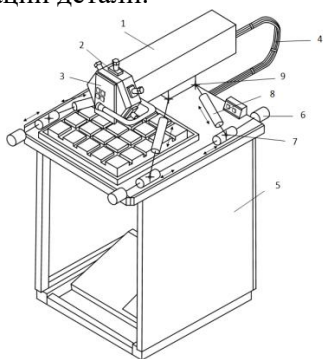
Резьбонарезной станок с револьверной головкой и МПС
